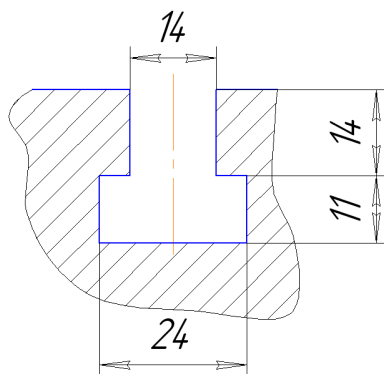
Т-пазы на столе станка для закрепления различных приспособлений
